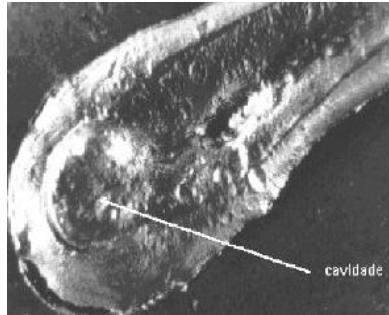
Deposição Insuficiente em juntas soldadas.
